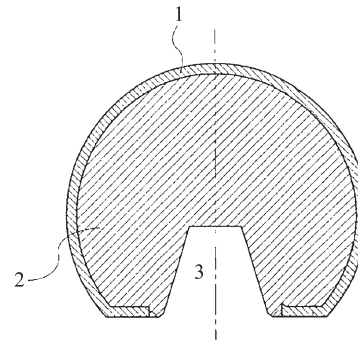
Поперечний переріз головки кульшового суглобу людини: 1 — металева оболонка; 2 — полімерна сердцевина; 3 — конусний отвір.
